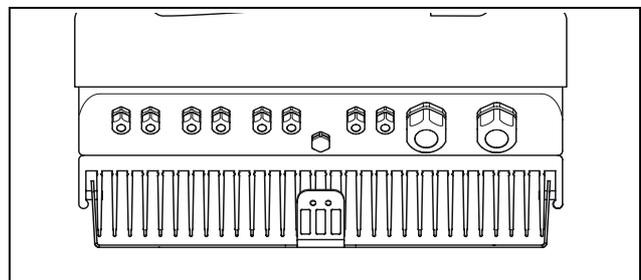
Befestigungsschraube eindrehen bei convert 8T/10T
